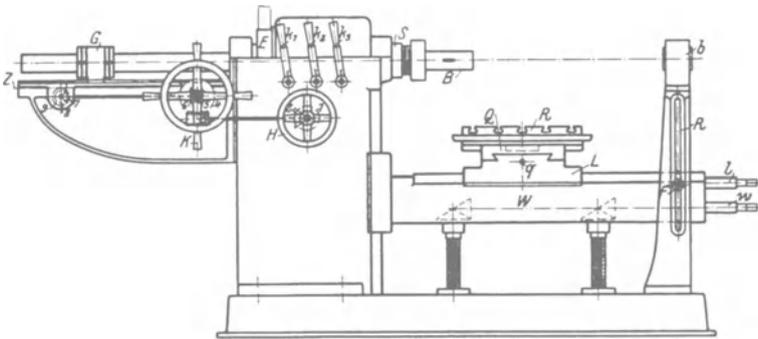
Waagrechtes Bohrwerk mit festliegender Spindel.
